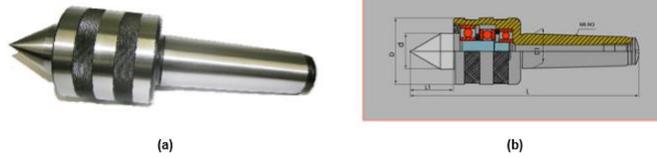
(a) Ponto rotativo, (b) Desenho técnico (Anon., 2014)
